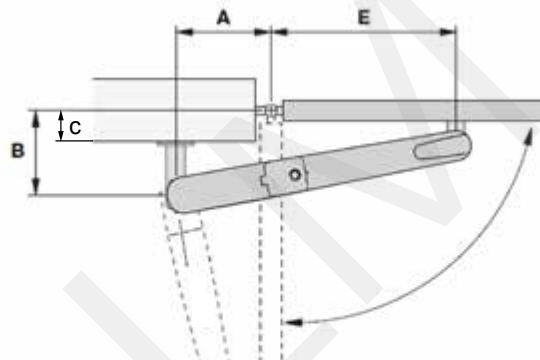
CZ - Zastoupení hodnoty «A» a «B»
